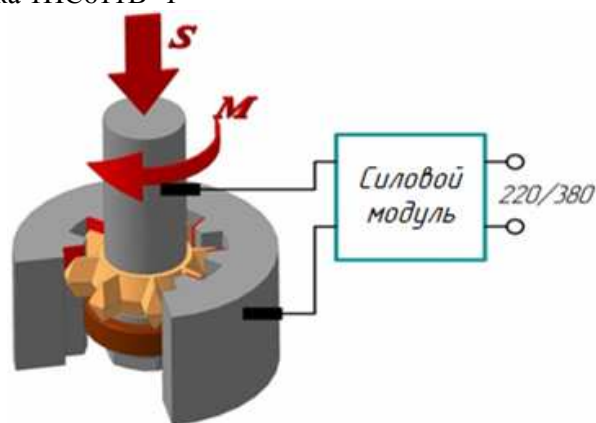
Схема процесса электромеханической закалки рабочих поверхностей шлицевой детали
